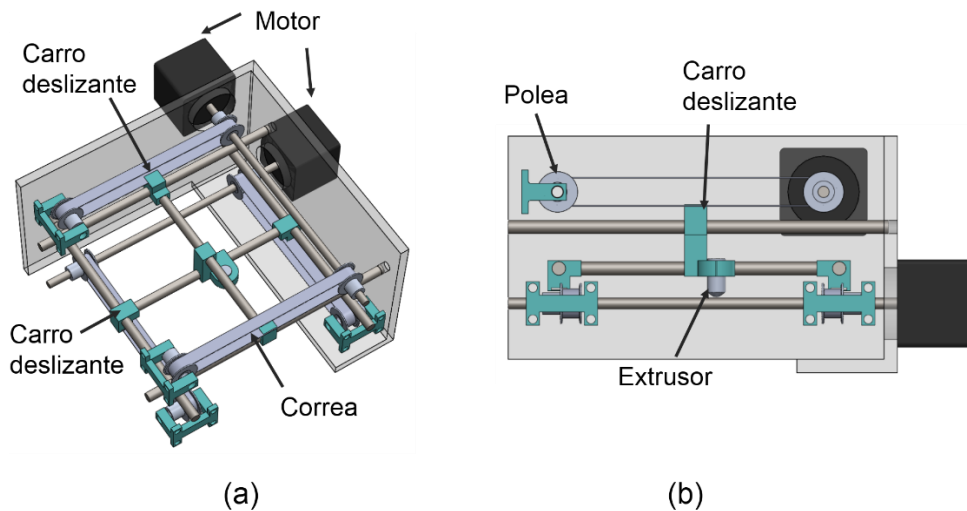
Partes que componen el sistema correa polea. (a) Vista isométrica y (b) vista alzada.
